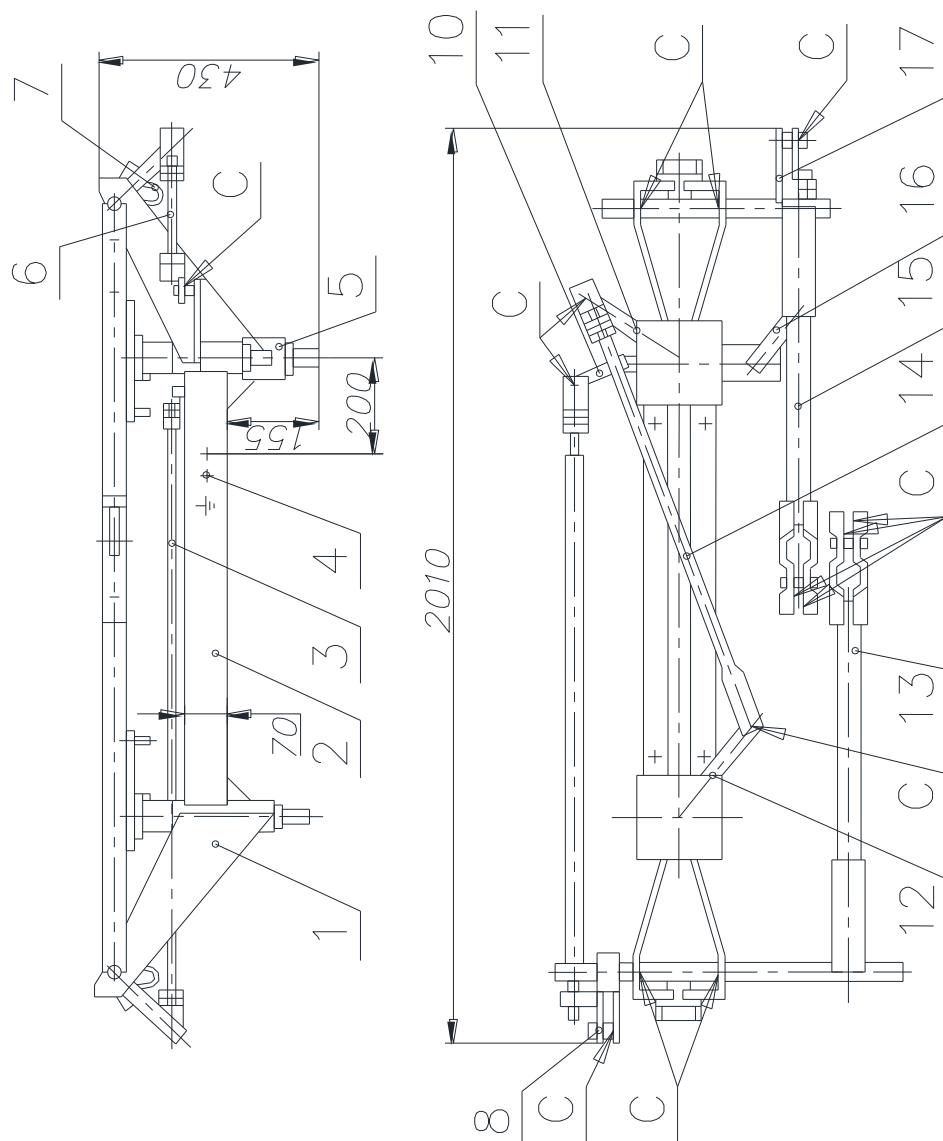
Габаритные размеры разъединителя RD32-110/1000 УХЛ
